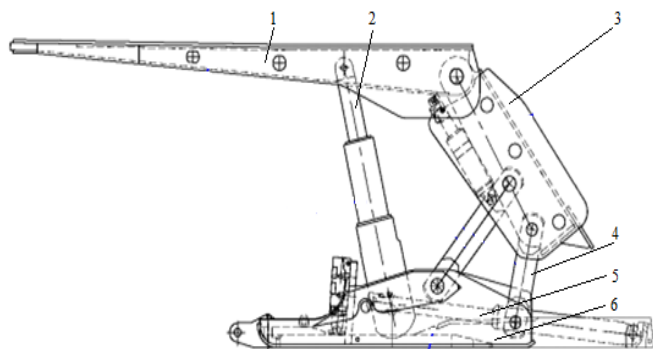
Типовая секция: 1-перекрытие, 2-гидростойки, 3-оградительный щит, 4-балансиры, 5-домкрат передвижки, 6-основание
